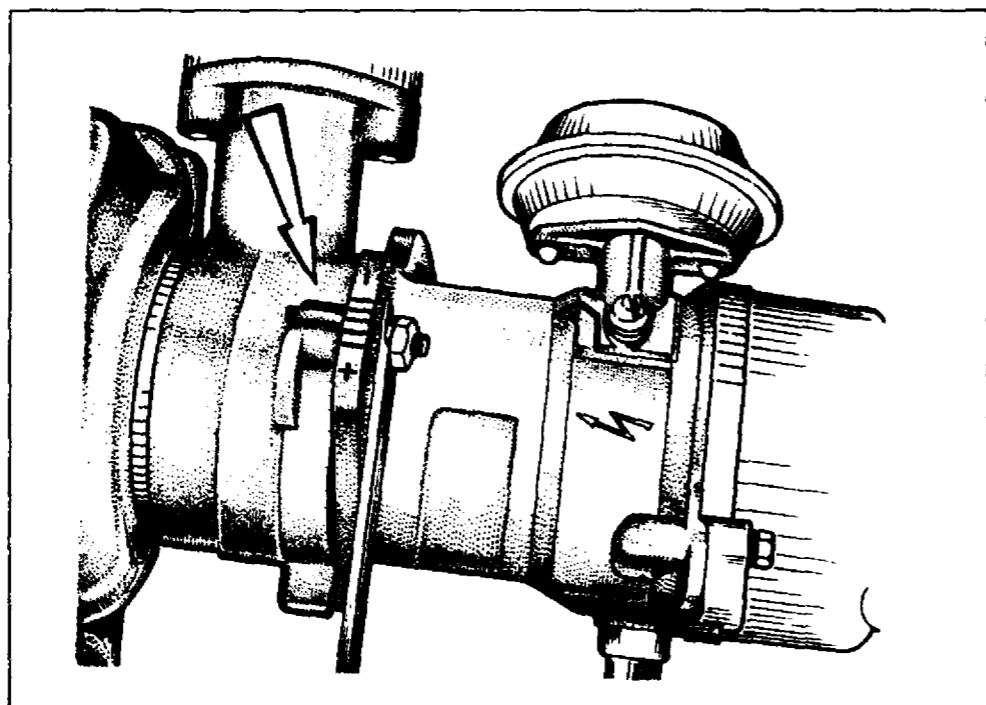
Установка датчика-распределителя зажигания. Стрелкой показан установочный выступ на корпусе вспомогательных агрегатов
